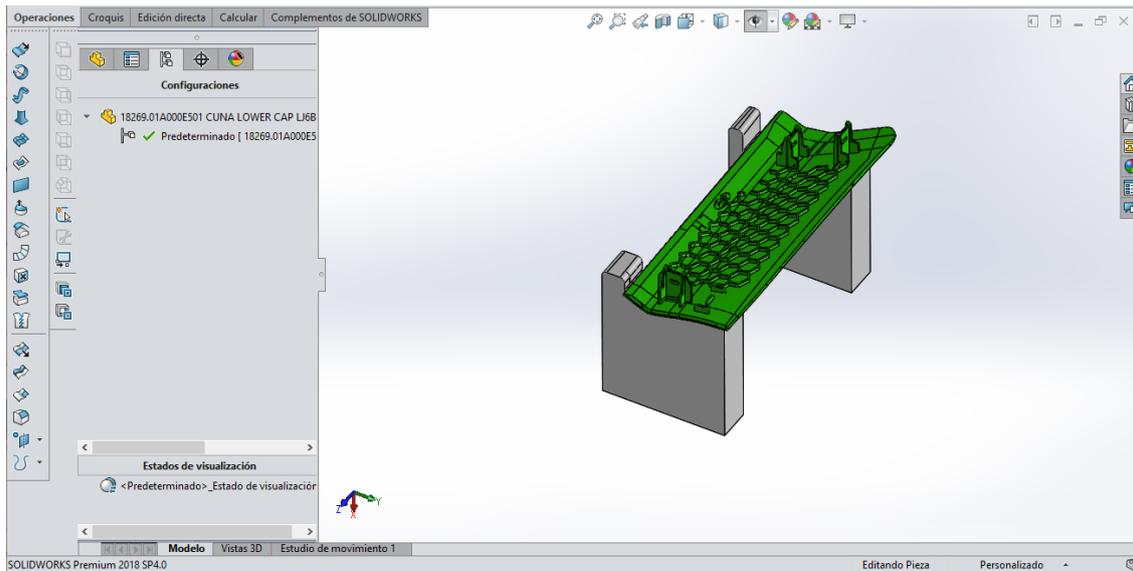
Cuna LOWER END PNL STRIP sin accesorios
